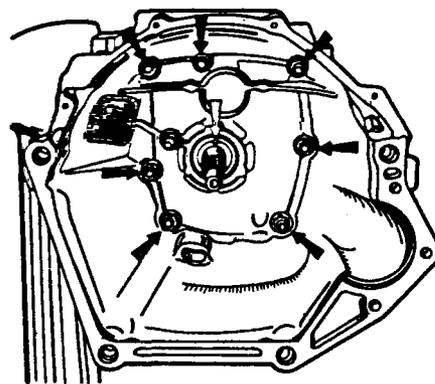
Внутренний вид картера сцепления. Черными стрелками указаны гайки крепления картера сцепления к коробке передач; белой стрелкой указано отверстие в передней крышке для выпуска масла из картера коробки передач, чтобы не происходило замасливание дисков сцепления
